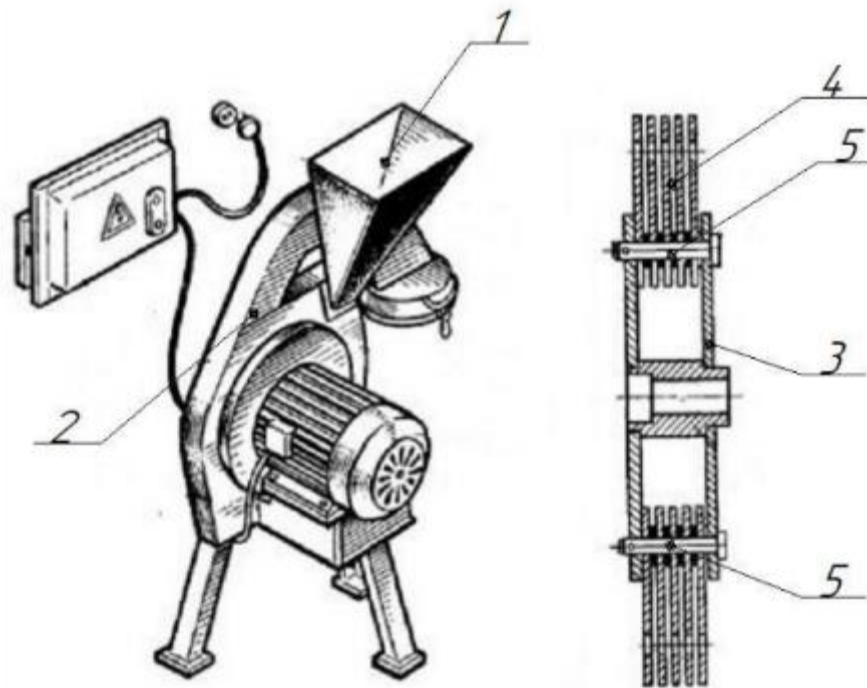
Дробарка зерна ДЗ-Т-1: 1 – завантажувальний бункер; 2 – корпус; 3 – ротор; 4 – молоток; 5 – палець
